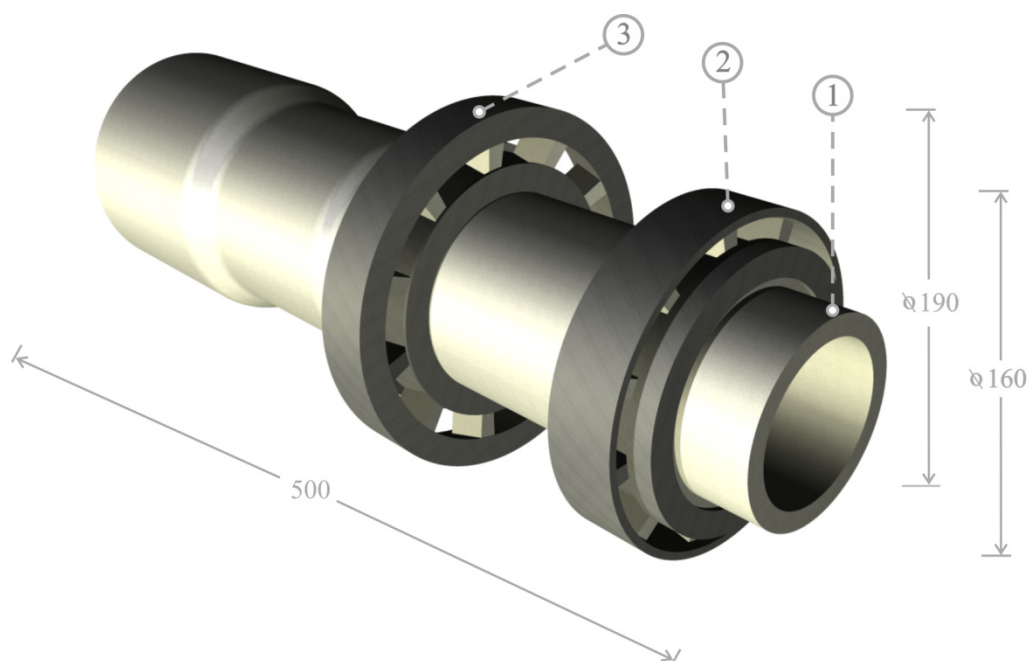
a – Geometrický model náboje se zvýrazněním upravených míst
